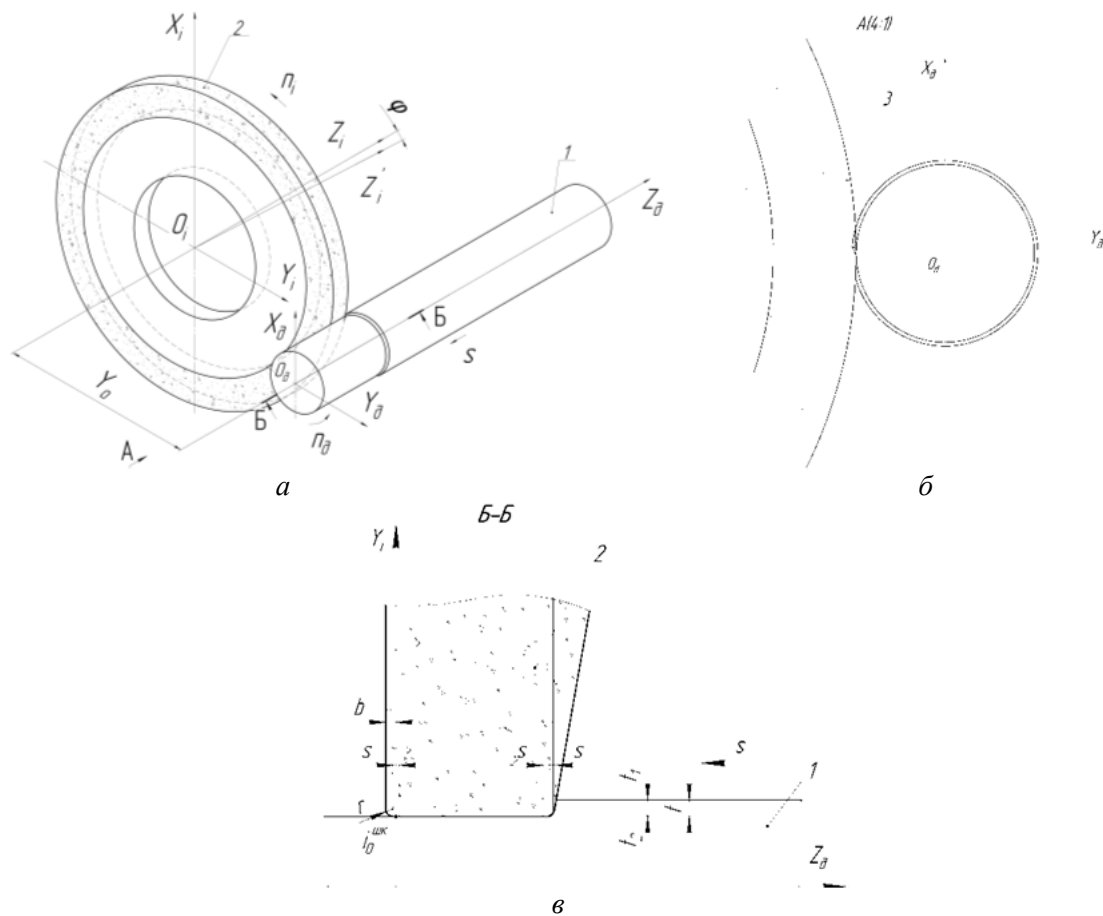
Схема глибинного однопрохідного шліфування циліндричного вала
